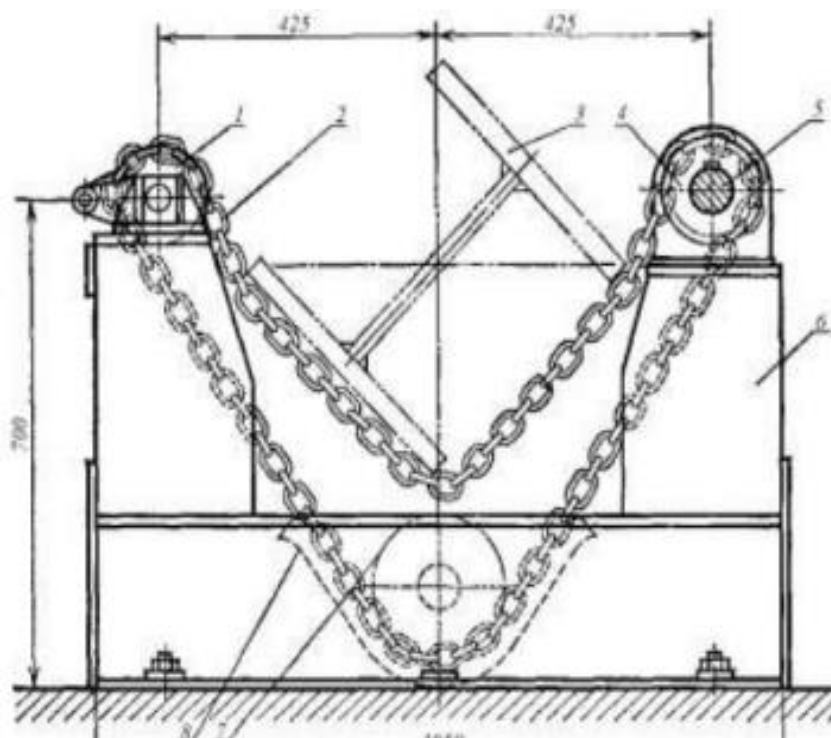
Загальний вигляд конструкції стаціонарного ланцюгового кантувача: 1, 4, 7 – ланцюгові блоки; 2 – замкнутий ланцюг; 3 – зварювана балка; 5 – приводний вал; 6 – опорні стояки; 7 – нижній блок; 8 – направляючий жолоб
